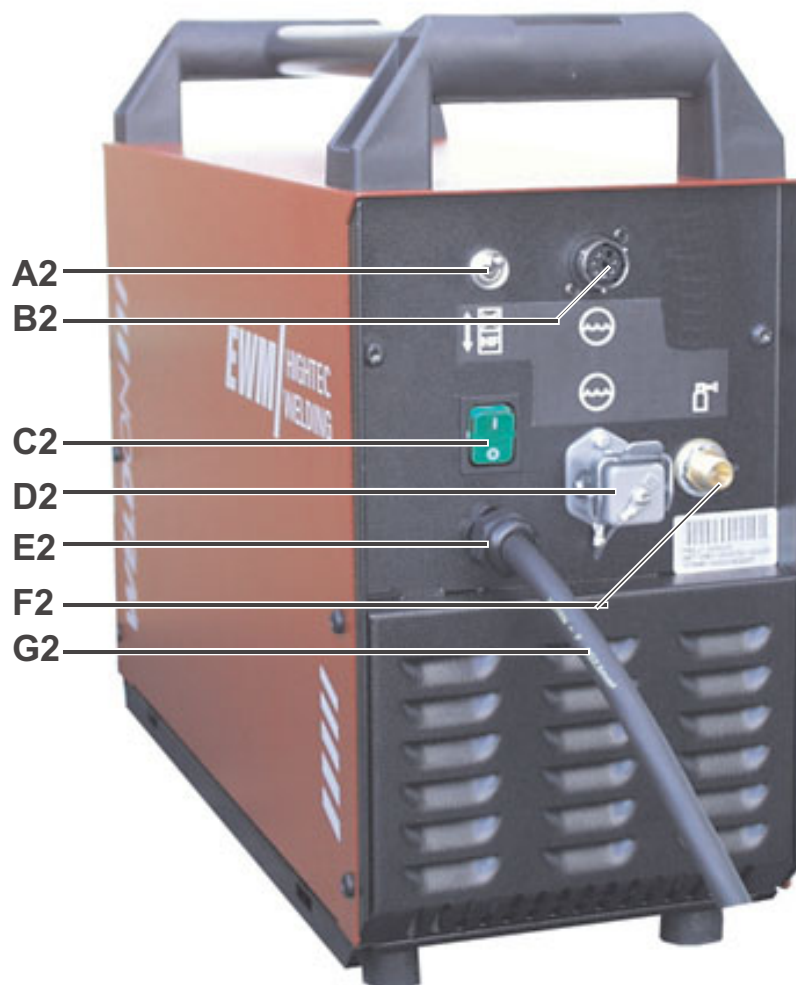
/2 Rückseite / Fig. 8/2 rear view
